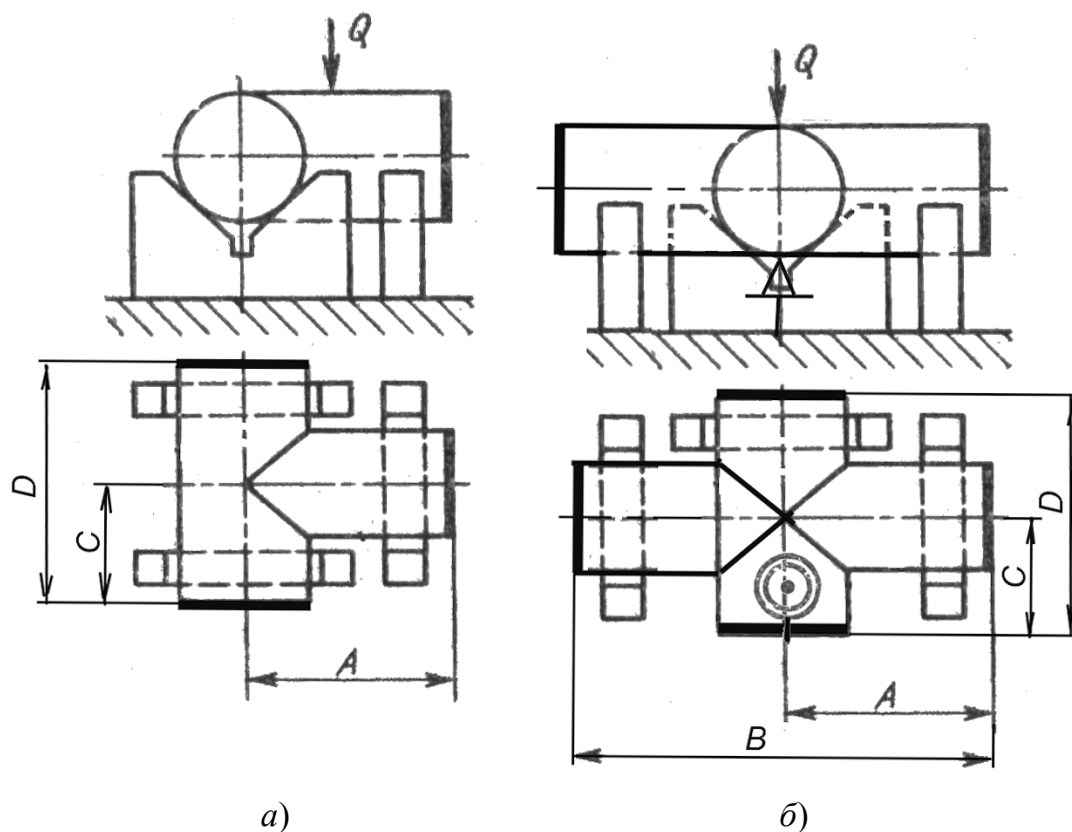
Установка заготовок с пересекающимися внешними цилиндрическими поверхностями
